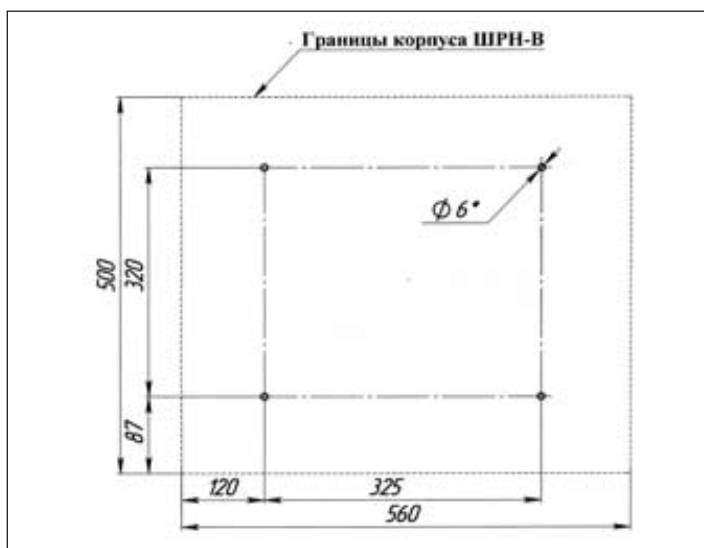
Разметка для крепления шкафа ШРН-В емкостью 300 пар
